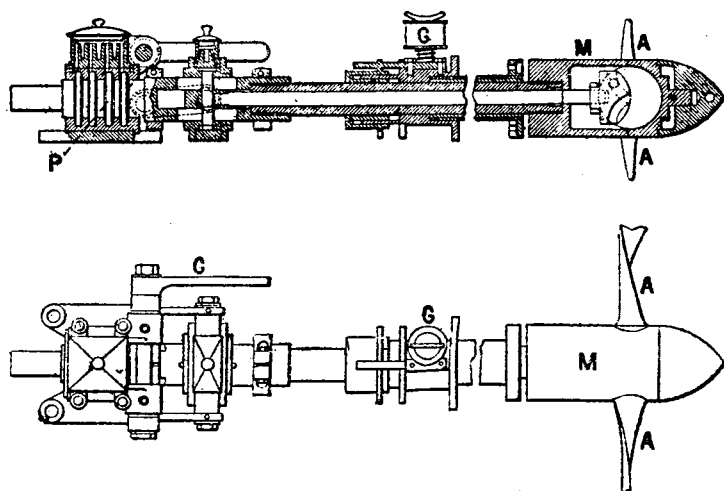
Винтъ съ поворотными лопастями *A* и гребной валъ съ приспособленіями для поворота лопастей.—*M*, втулка винта, заключающая механизмъ для поворота лопастей.—*P*, упорный кольцевой подшипникъ. Кольца расположены въ рядъ для распредѣленія давленія.—*G*, штаufferъ для смазки направляющаго сплошнаго подшипника.—*C*, рычагъ для поворота лопастей.
